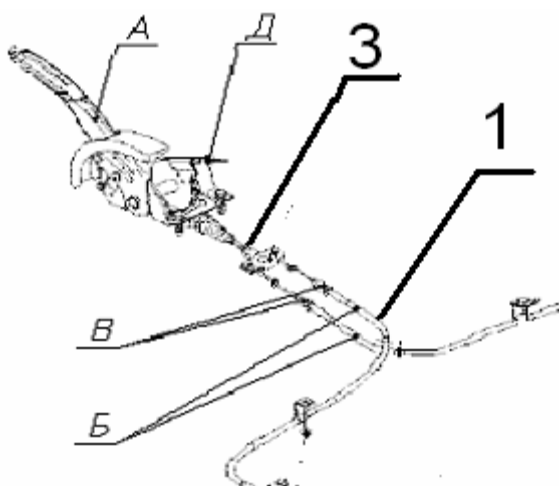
Крепление крышки консоли и стояночный тормоз.
